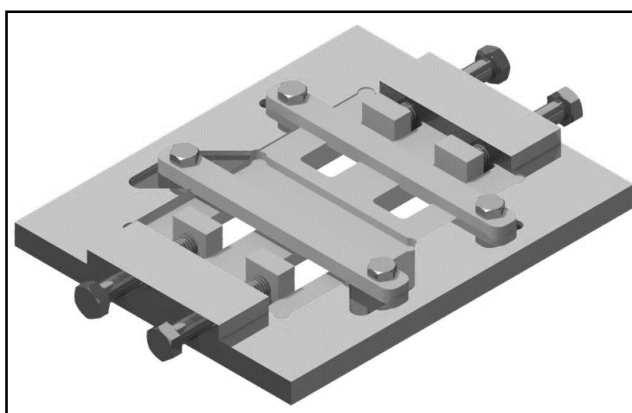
Esquema del diseño del sujetador de cupones de A6061-T6 y DP900
